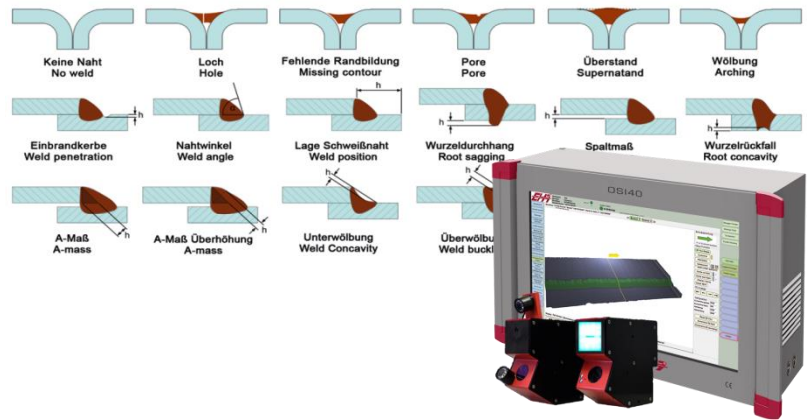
Schweißnaht: Optisches Erscheinungsbild erlaubt Rückschlüsse auf Qualität
